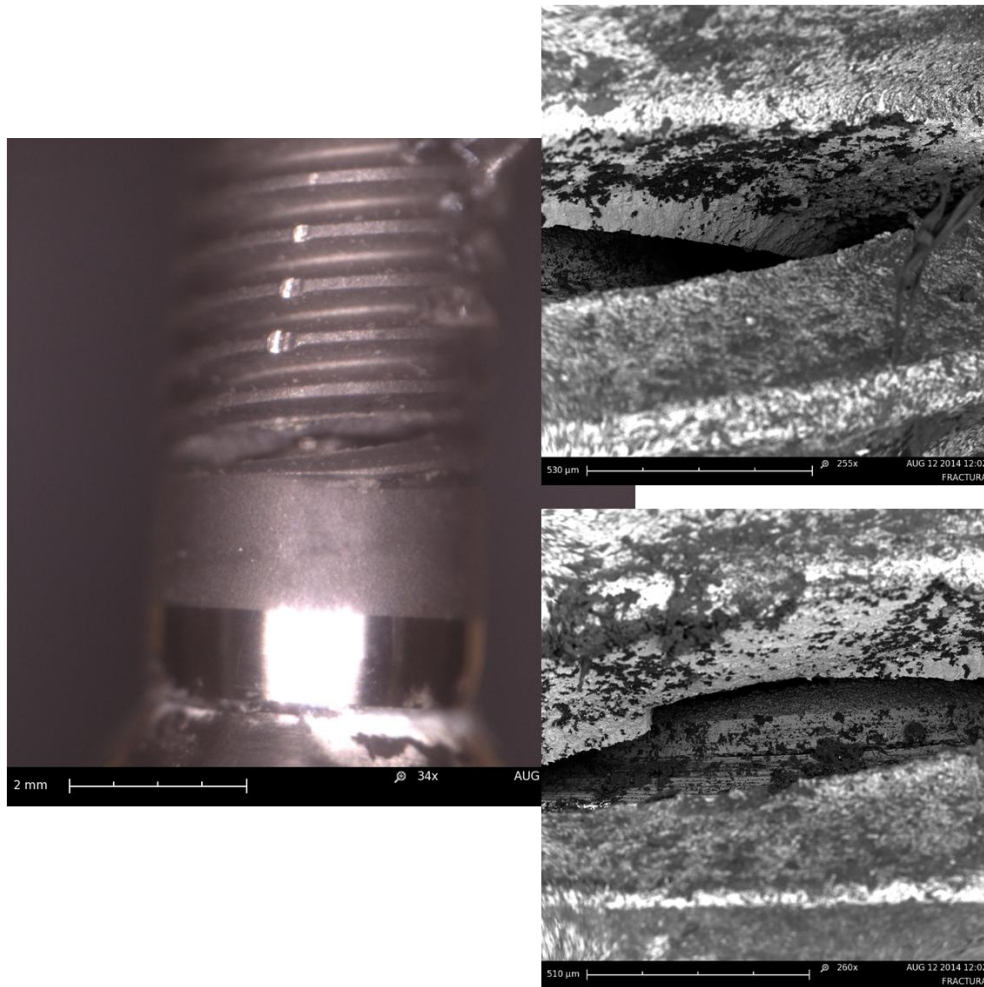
Imagen de probeta en la que se identifica la fractura horizontal del implante en las imágenes de la derecha bajo MEB.
